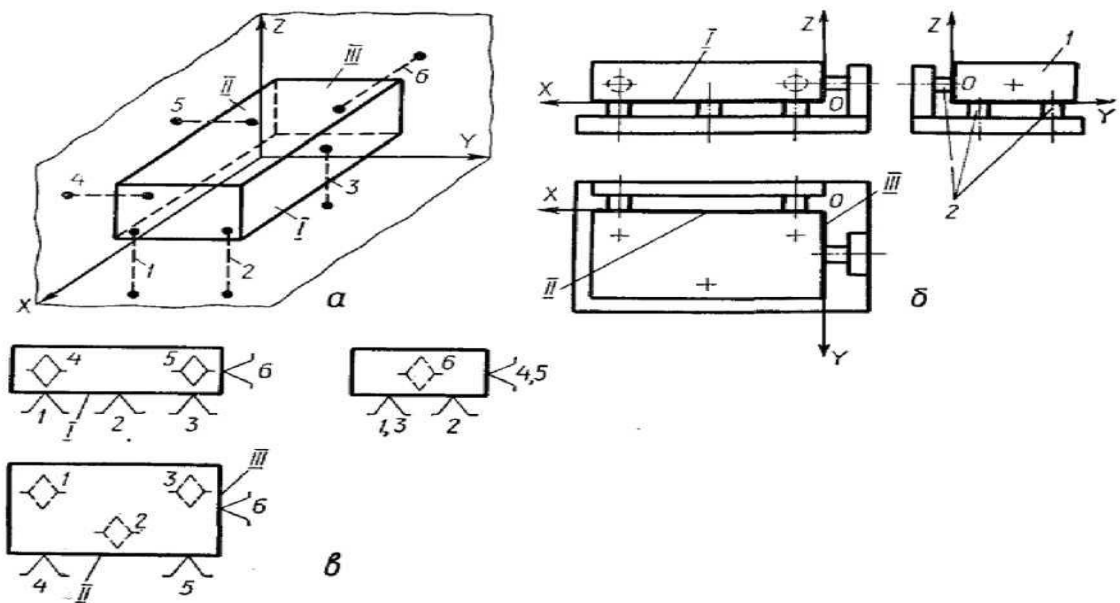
Схема базування заготовки по правилу 6-ти точок
